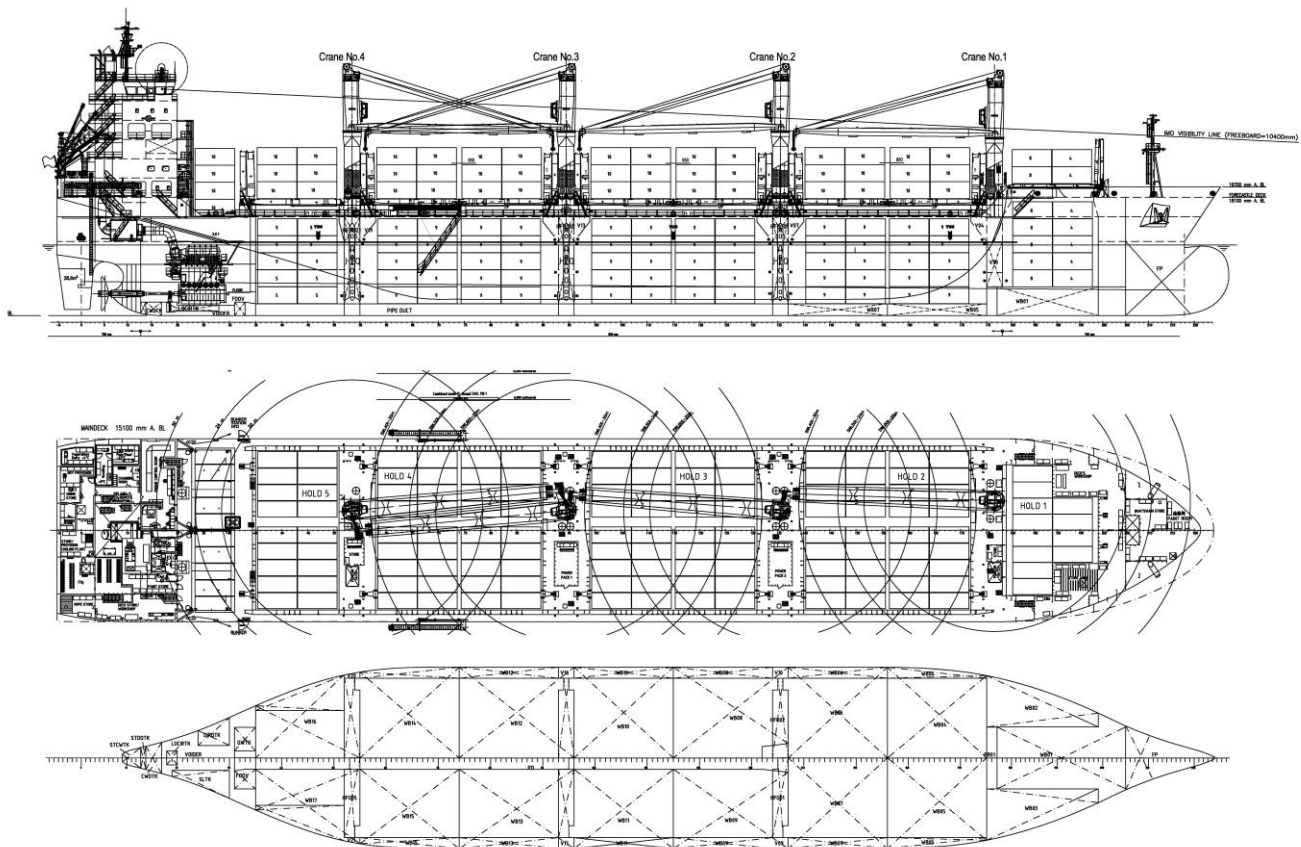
Загальний вигляд балкера “WARNOW MARS”
